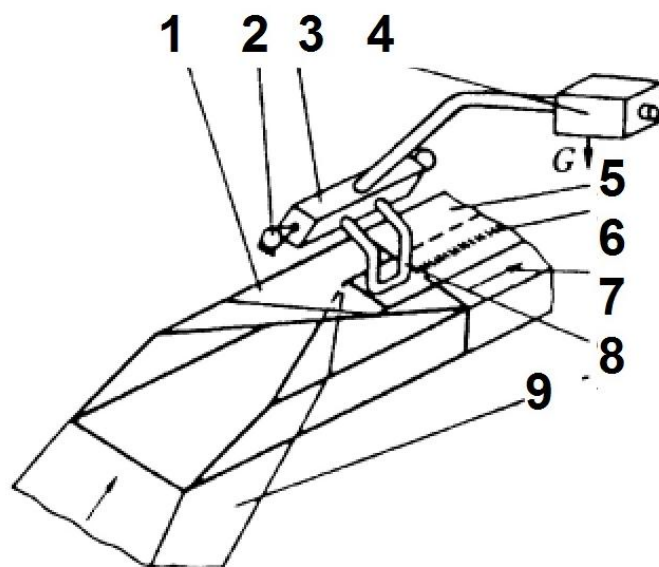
Безперервне зварювання за допомогою зварювальної скоби
